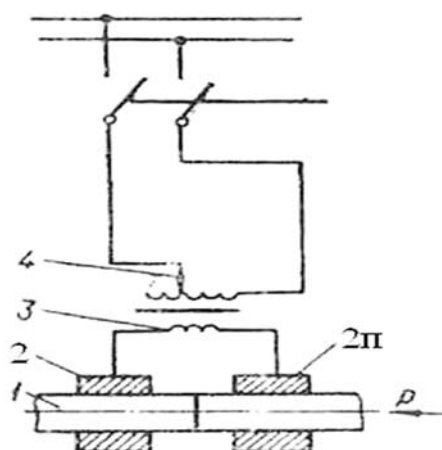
Схема стыковой сварки давлением
